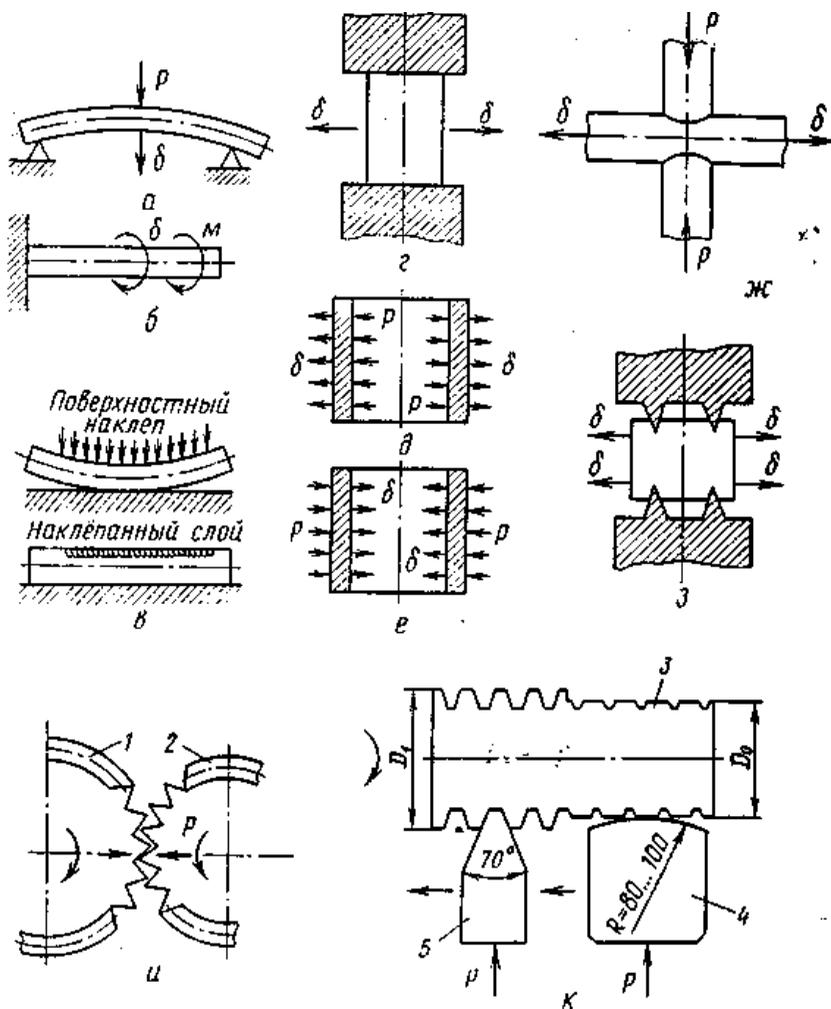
Схемы ремонта деталей пластическим деформированием:
